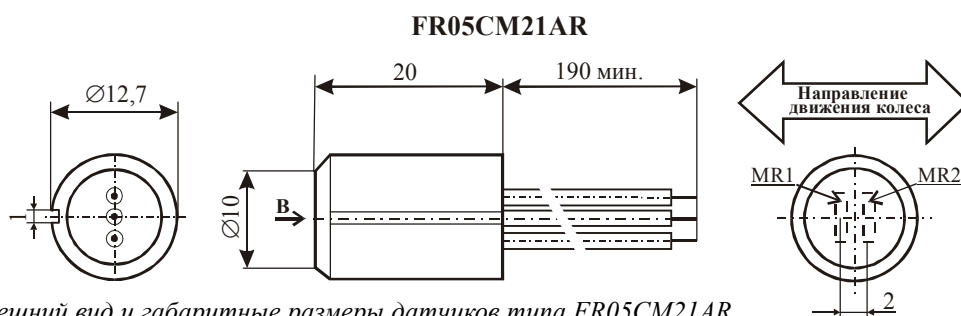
Внешний вид и габаритные размеры датчиков типа FR05CM21AR
